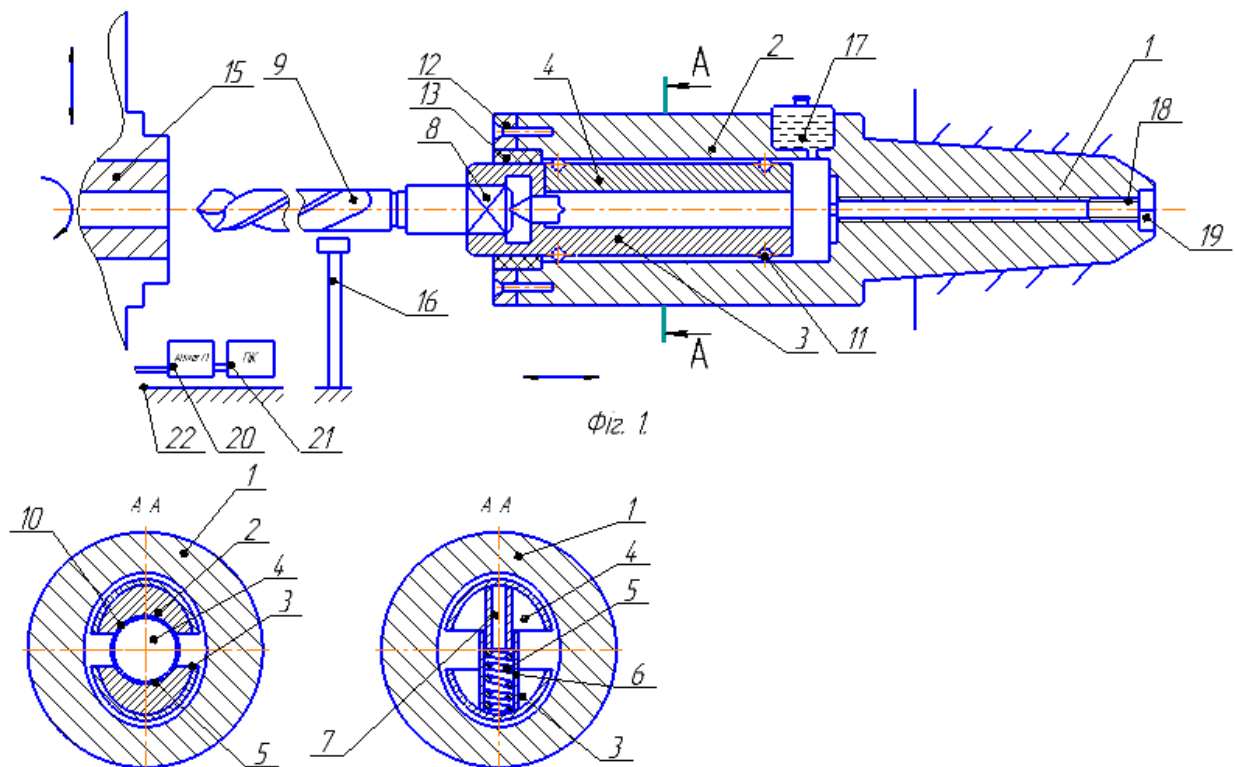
Конструкція патрона для обробки деталей пальцевим ріжучим інструментом
